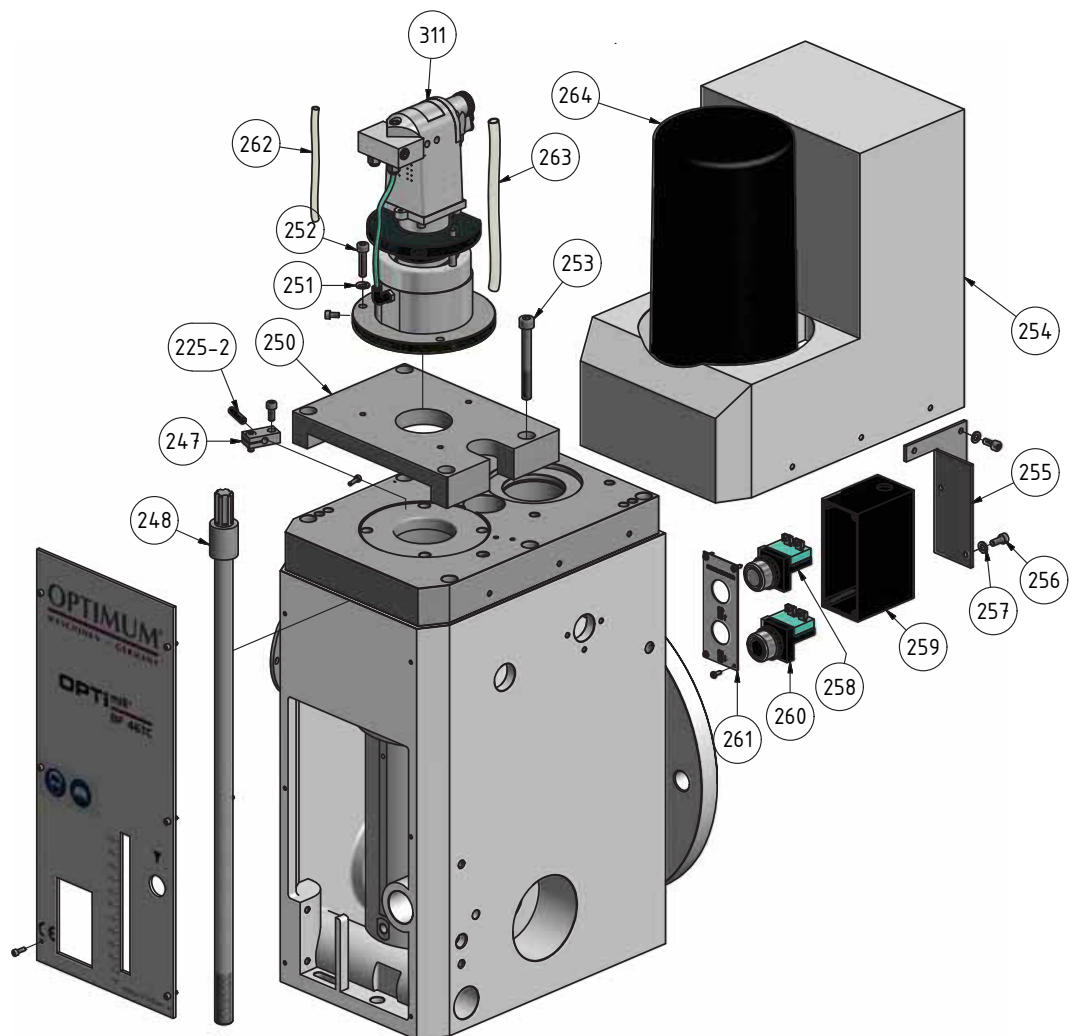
Fräskopf - Milling head BF46 TC Vario
